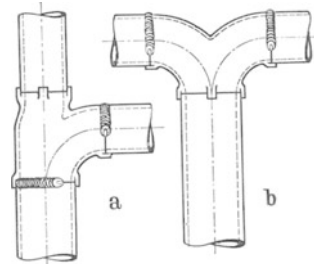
Schweißungen an Stahlgußfittings.
